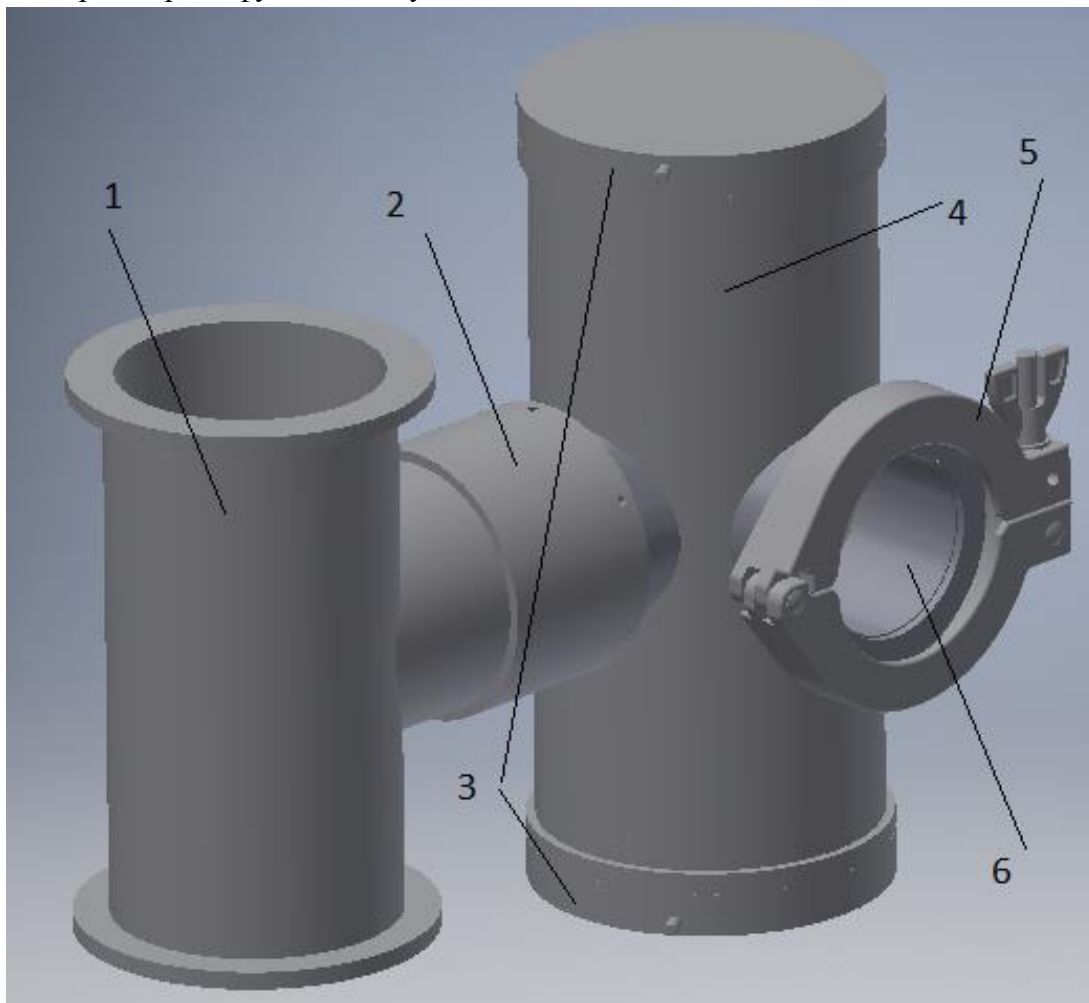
3D-модель Т-образной рабочей камеры из нержавеющей стали:
